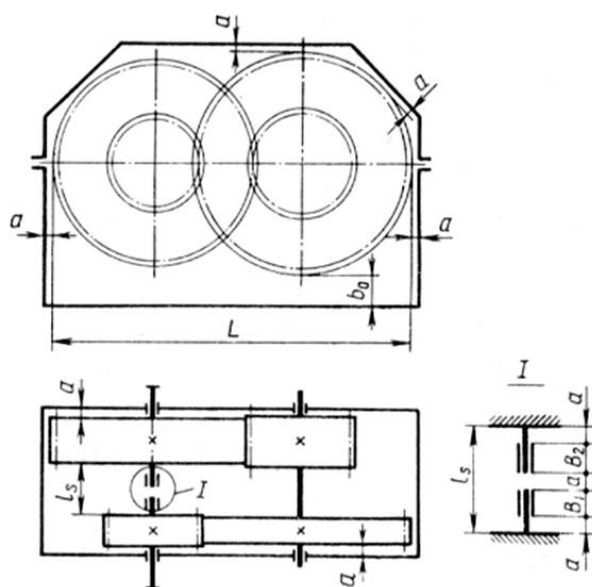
Редуктор цилиндрический двухступенчатый соосный
